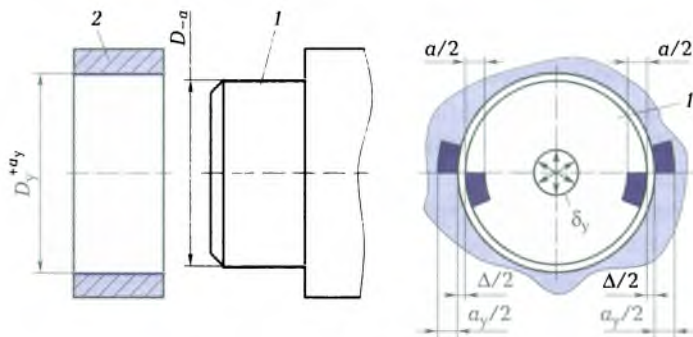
Схема установки базы «вал» в установочный элемент приспособления — цилиндрическое отверстие:
